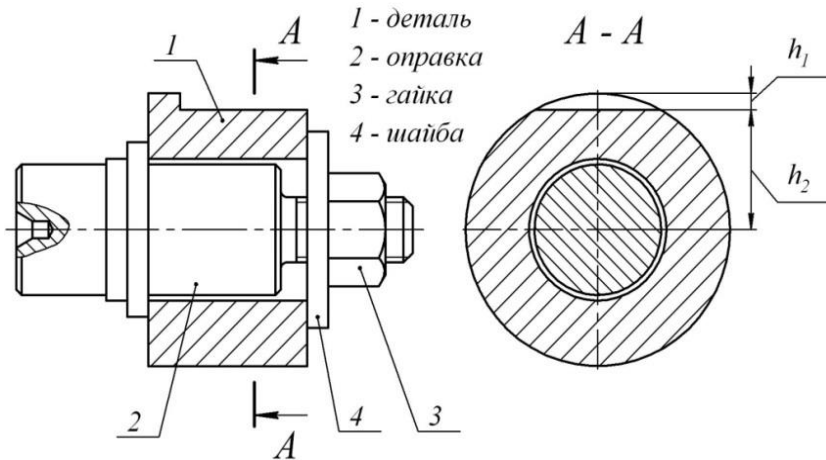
Базування деталі на циліндричній оправці з рівномірним зазором
